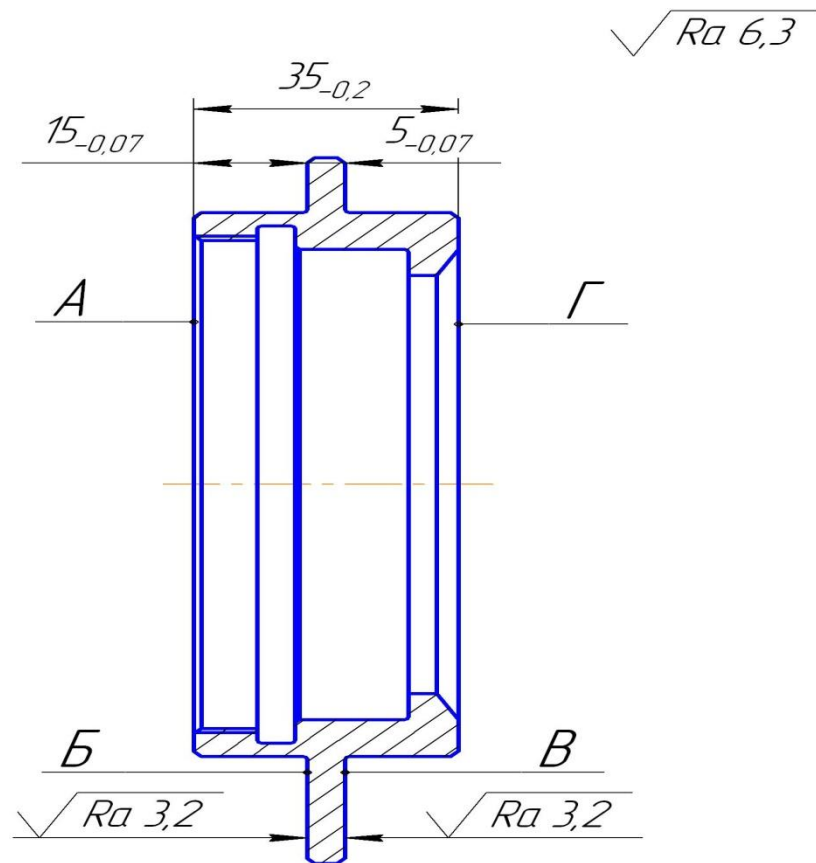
Ескіз деталі з позначенням торцевих поверхонь
